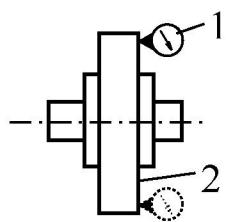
Схема измерения торцового биения обода ленточнопильного станка
